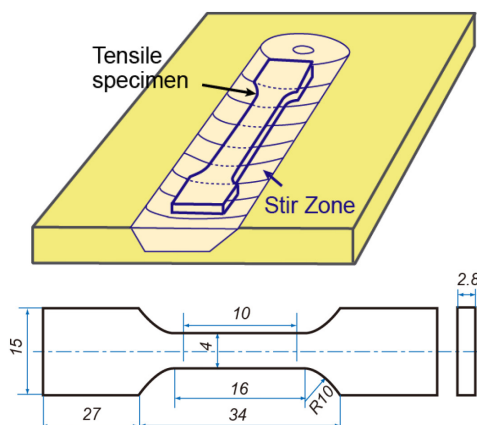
Schematic view and dimensions(mm) of the tensile test specimen
